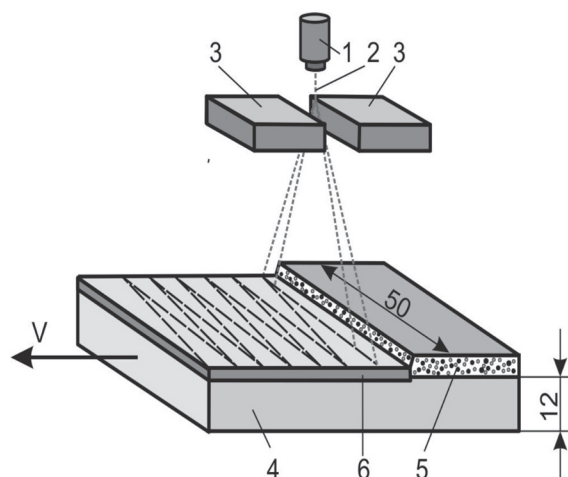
Схема электронно-лучевой наплавки алюминиево-титановой смеси на заготовки из сплава ВТ1-0:
